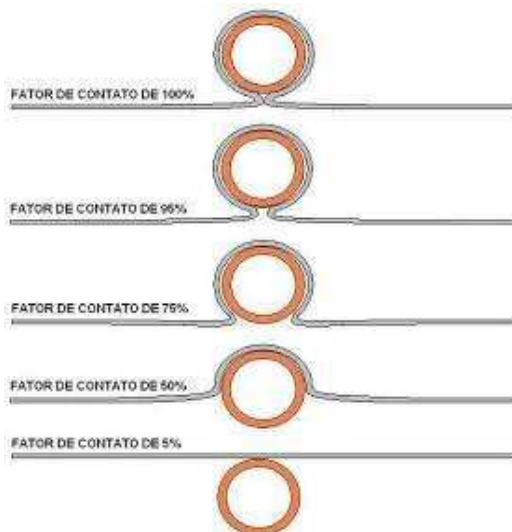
Exemplos de fator de contato entre Placa Absorvedora e Serpentina
